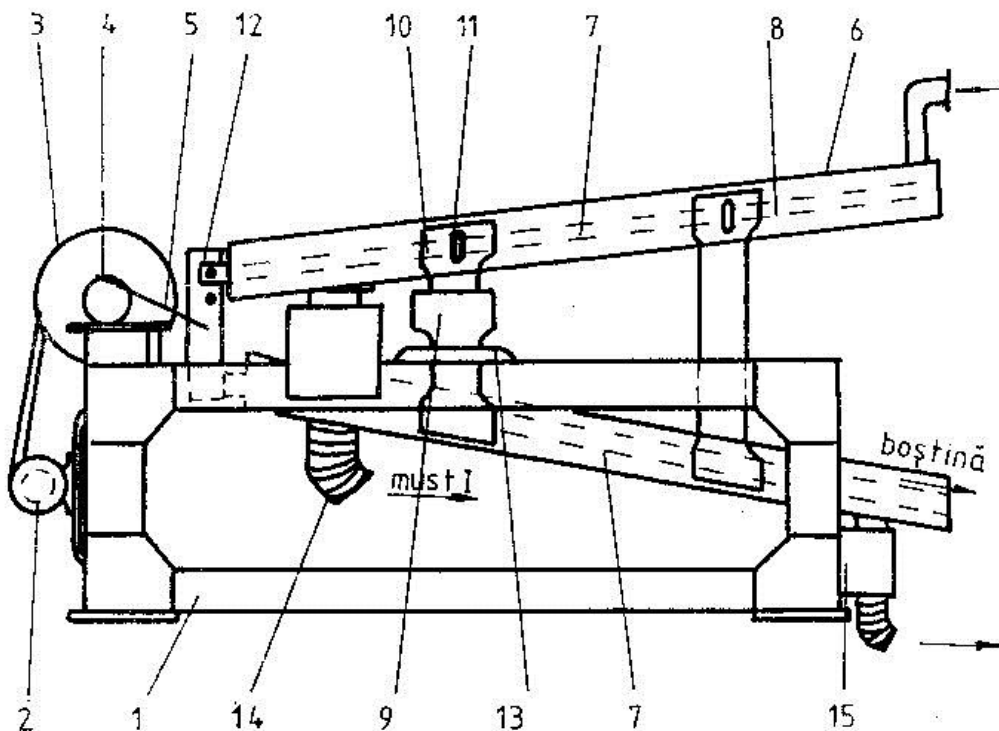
Scurgător oscilant: 1- cadru mașină; 2- motor electric; 3- transmisie cu curele trapezoidale; 4- arbore cu excentric; 5- bielă; 6- ramă înclinată; 7- sită; 8- cadru colector; 9- jgheab; 10- traversă; 11- dispozitiv de strângere; 12- mecanism de schimb; 13- glisieră; 14- ștuț pentru scurgere must I; 15- ștuț scurgere must II.
